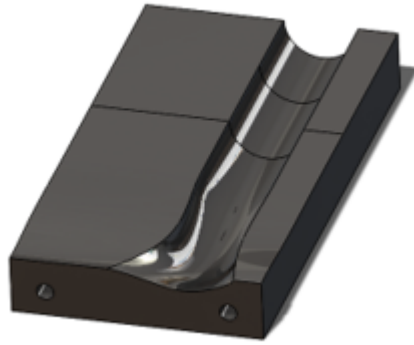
Vue détaillée d’une section du moule de la pale d’éolienne avant assemblage
